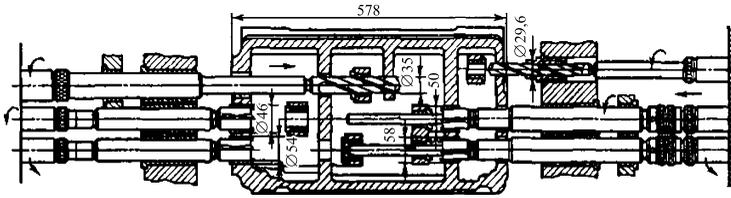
Схема сверления и растачивания на двухстороннем агрегатном станке
